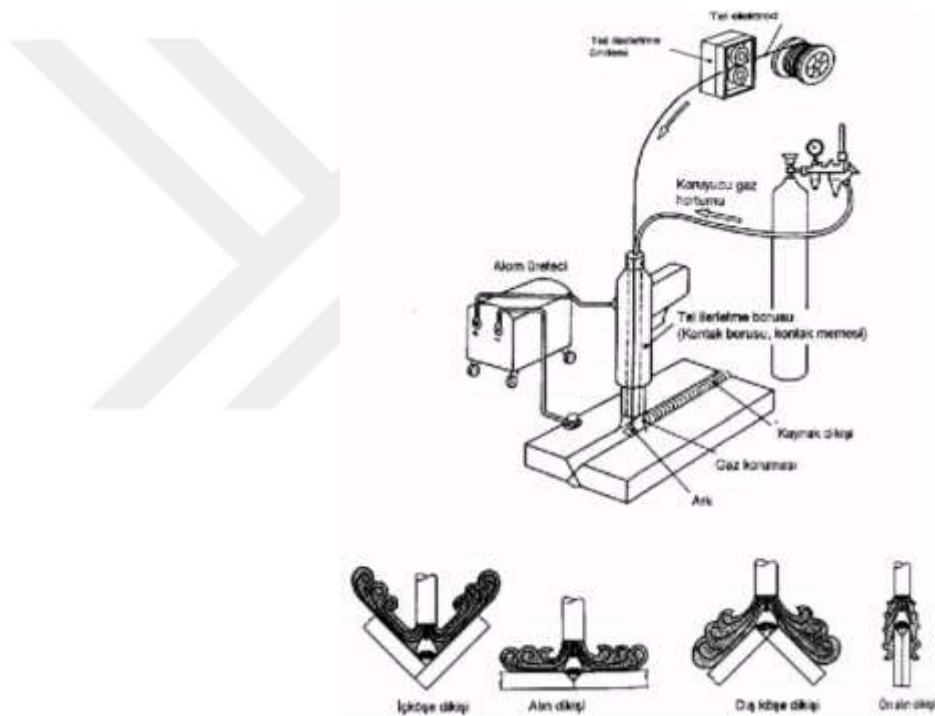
Gazaltı kaynak yönteminde ark bölgesi
